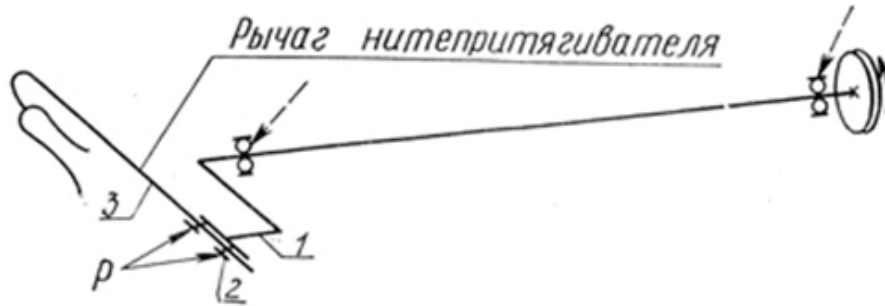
Кинематическая схема механизма нитепритягивателя машины 97-А класса: 1 — палец кривошипа, 2 — винты для жесткого закрепления рычага нитепритягивателя, 3 — рычаг нитепритягивателя
